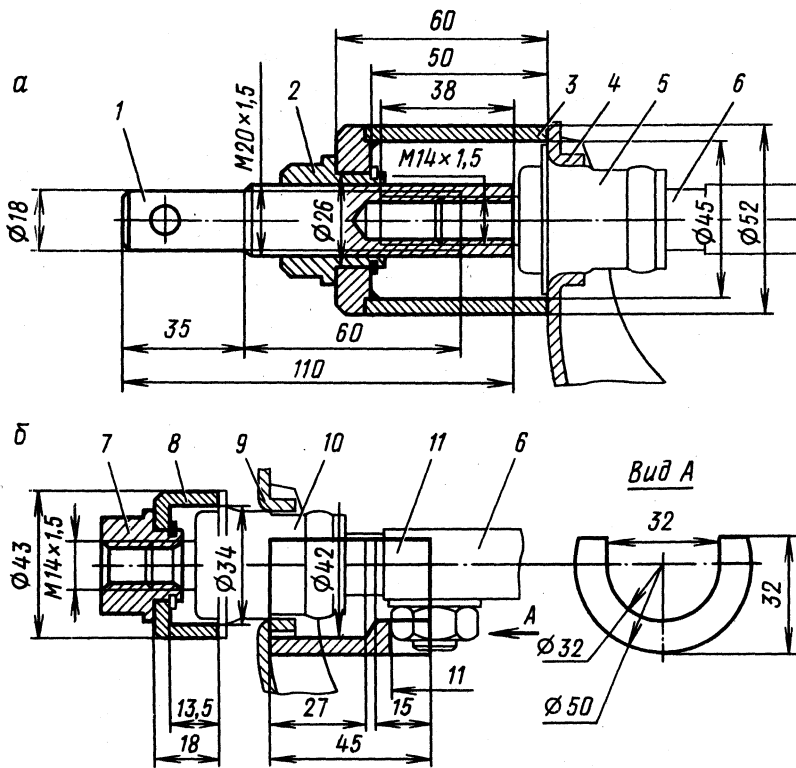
Перепрессовка резинометаллических шарниров нижнего рычага передней подвески автомобиля «Жигули»:
